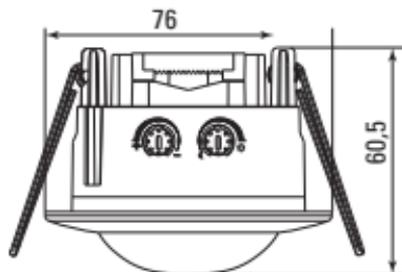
Габаритные и установочные размеры датчика MS-100
